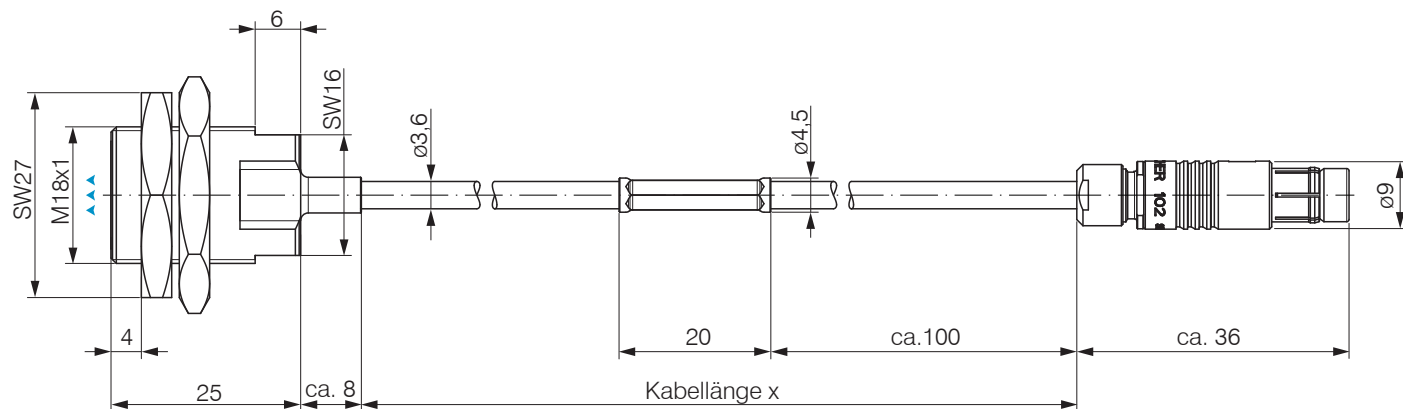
Maßzeichnung Sensoren ES-S4-C-CaX/mB0, Abmessung in mm
